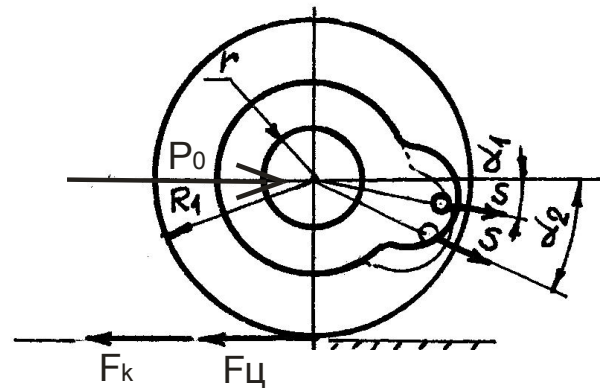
Розрахункова схема колеса візка з різним напрямком рушійної сили / Fig. 1. The design scheme of the wheel of the cart with different in-directional driving force
